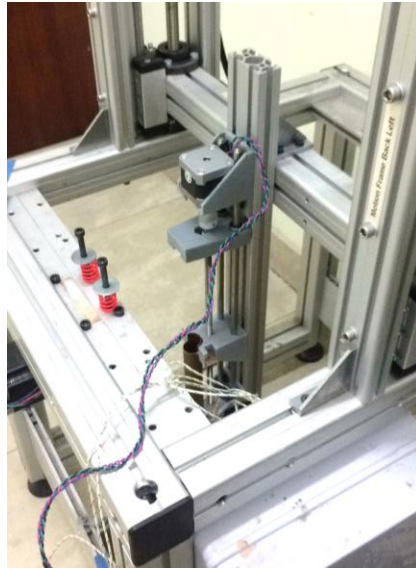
Montaje del prototipo extrusor sobre la impresora ILIOS.
